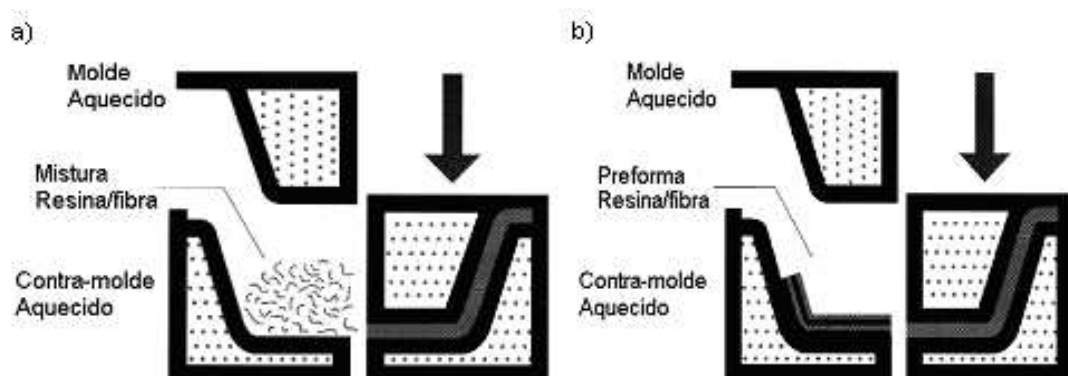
Moldagem por compressão: métodos a)BMC e b)SMC [6].
